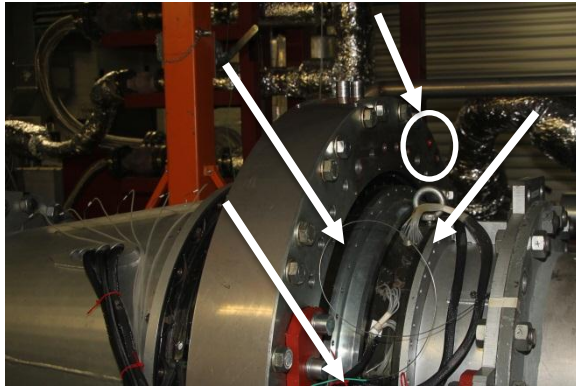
Kennzeichnung der zu entfernenden Schrauben für die Demontage der Außenkontur des Zwischendiffusers
